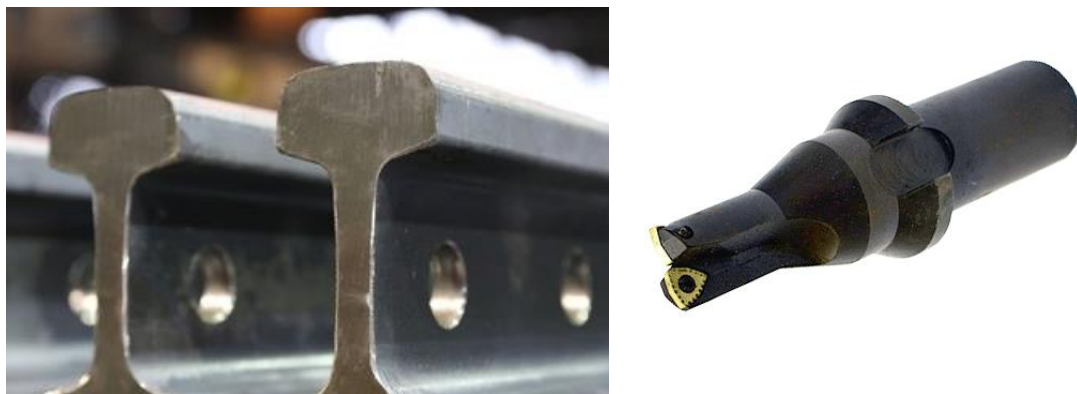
Сверла рельсовые с механическим креплением сменных твердосплавных пластин
